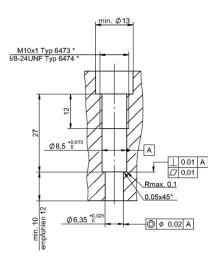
Bohrung für Direkteinbau mit Montagenippel
